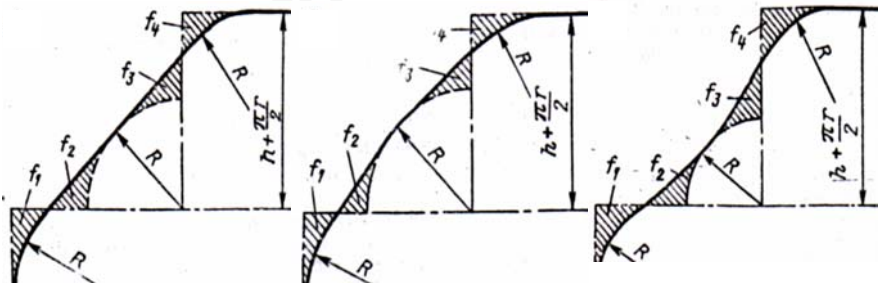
Побудова контура заготовки для низьких прямокутних коробок, що витягаються за одну операцію:
